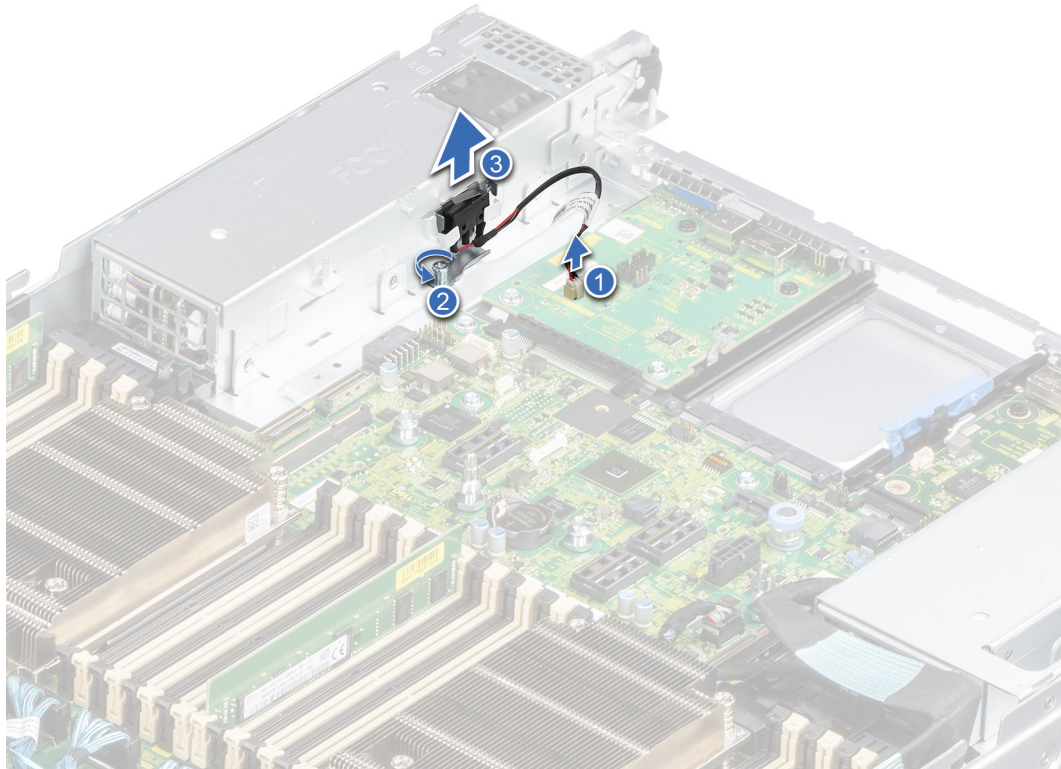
Entfernen des Eingriffsschaltermoduls
